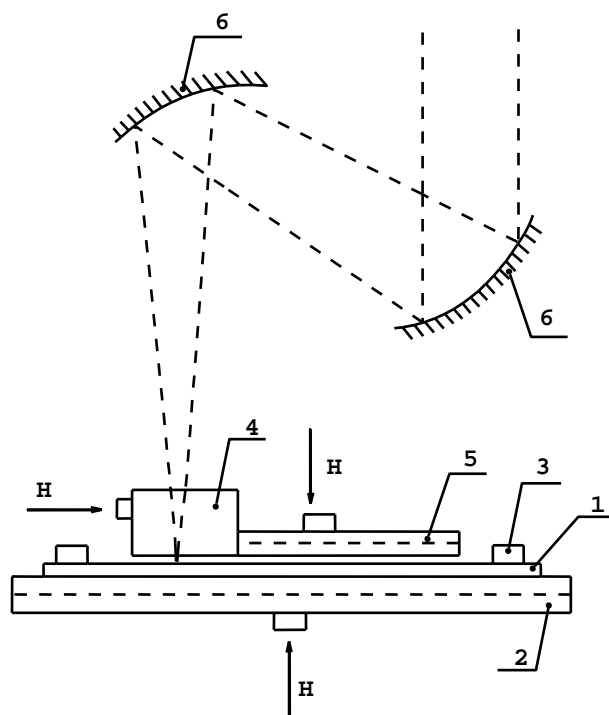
Схема лазерной сварки: 1 – образец; 2 – опора; 3 – прижим; 4 – сопло; 5 – козырек; 6 – зеркала фокусирующего объектива Кассегрена
